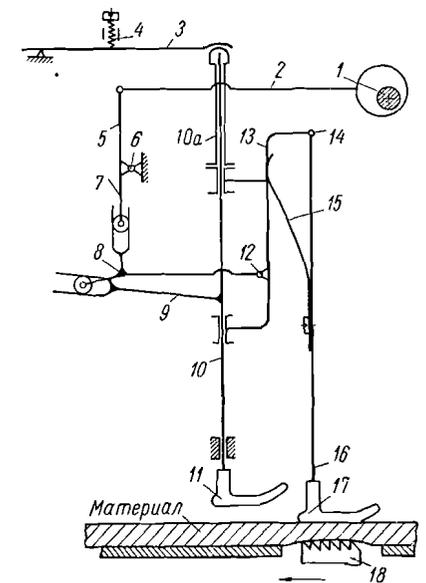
Схема механизма перемещающейся лапки машины 48-го класса ПМЗ
